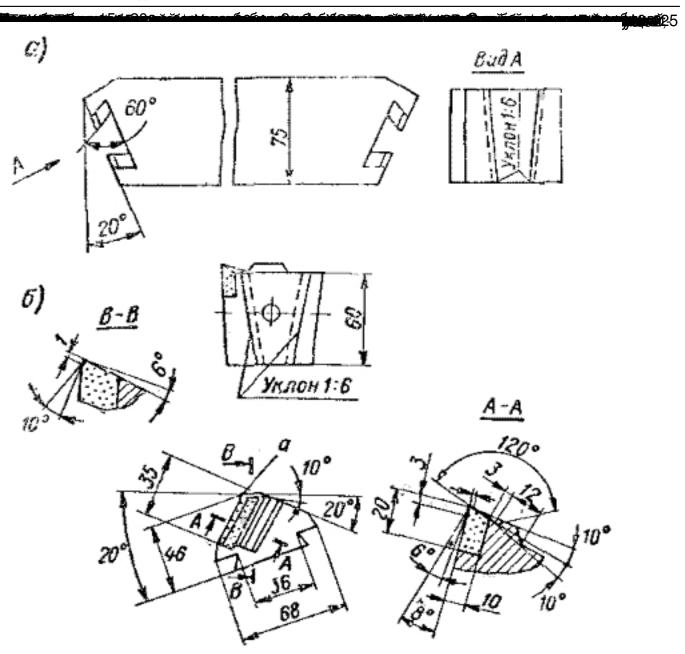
Сборный резец конструкции УЗТМ: а — державка; б — режущие вставки,
